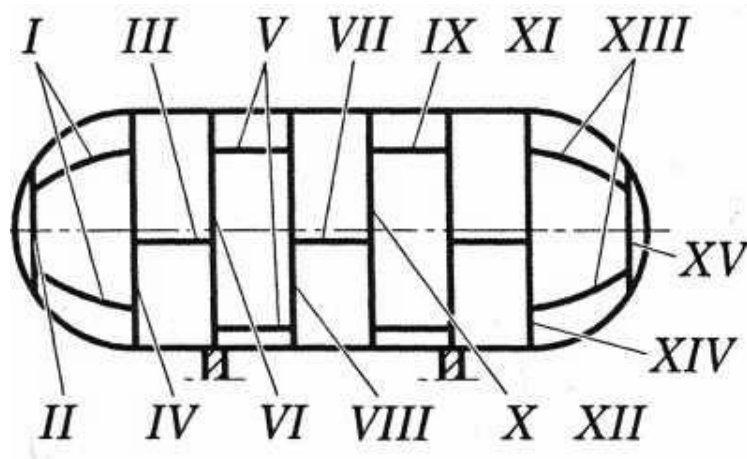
Схема зварювання циліндричних конструкцій [1]:
